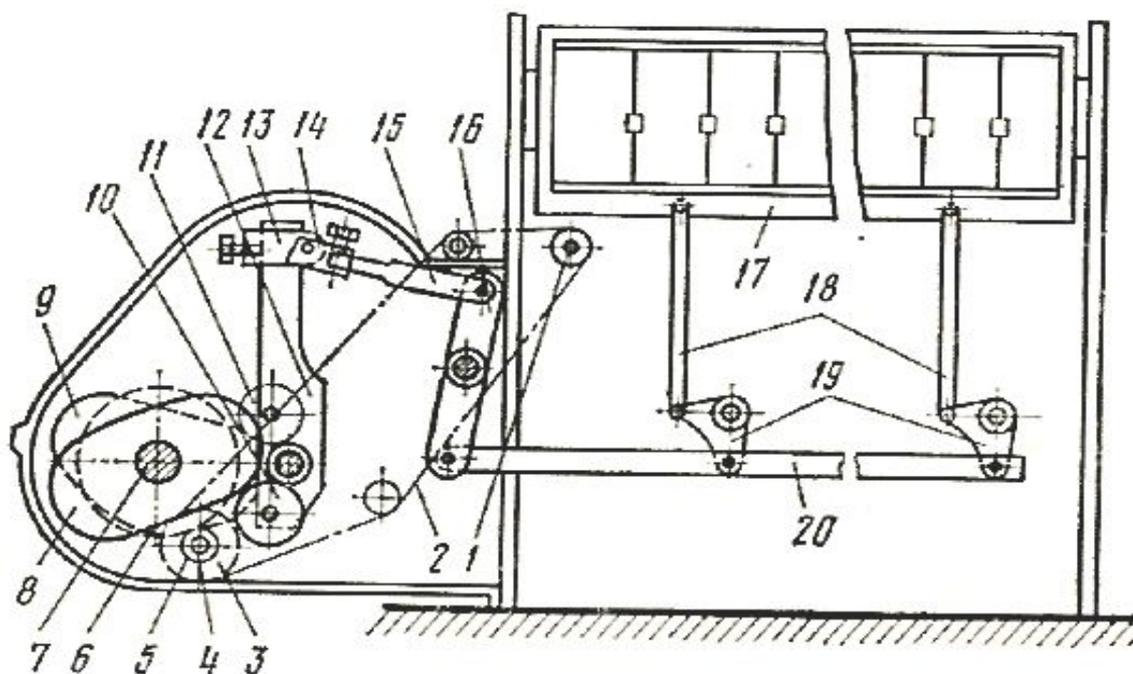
ЗевООобразовательный механизм: 1- поперечный вал, 2- цепь, 3- звездочка, 4- валик, 5 и 6 – шестерни, 7- кулачковый вал, 8 и 9 – спаренные кулачки, 10 и 11 – ролики, 12- рычаг, 13- хомут, 14- серьга, 15- тяга, 16- двуплечий рычаг, 17 – ремизная рама, 18- вертикальные тяги, 19- угольники, 20- горизонтальная тяга.
